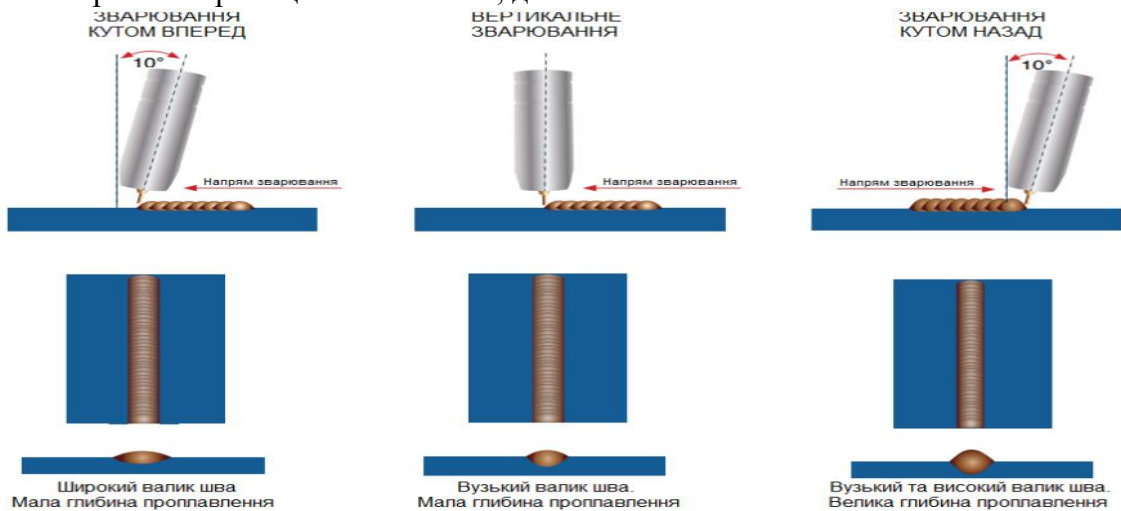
Вплив нахилу пальника на формування валика та провар шва
